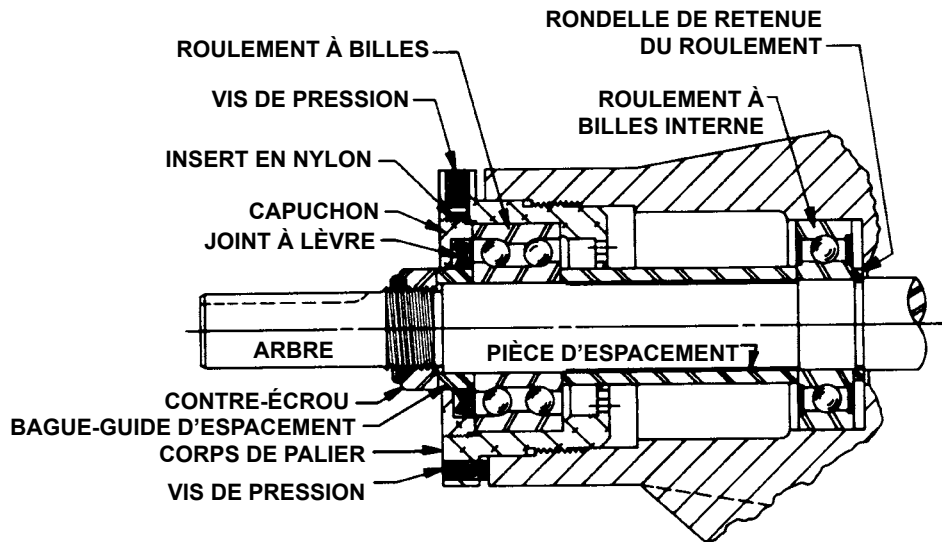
ENSEMBLE PALIER DE BUTÉE, TAILLE AS, AK ET AL
